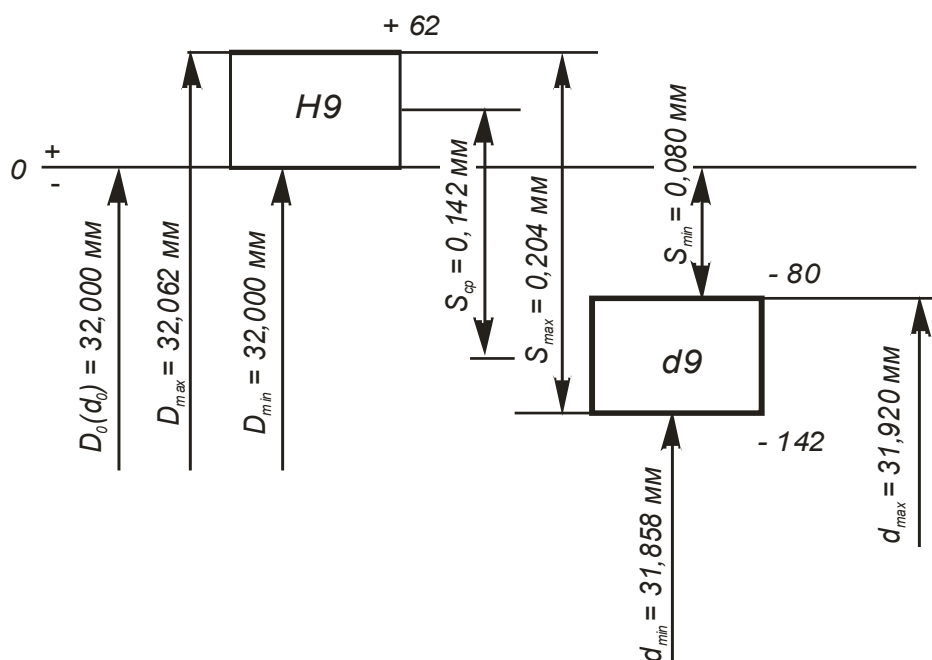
Схема расположения полей допусков вала и втулки
